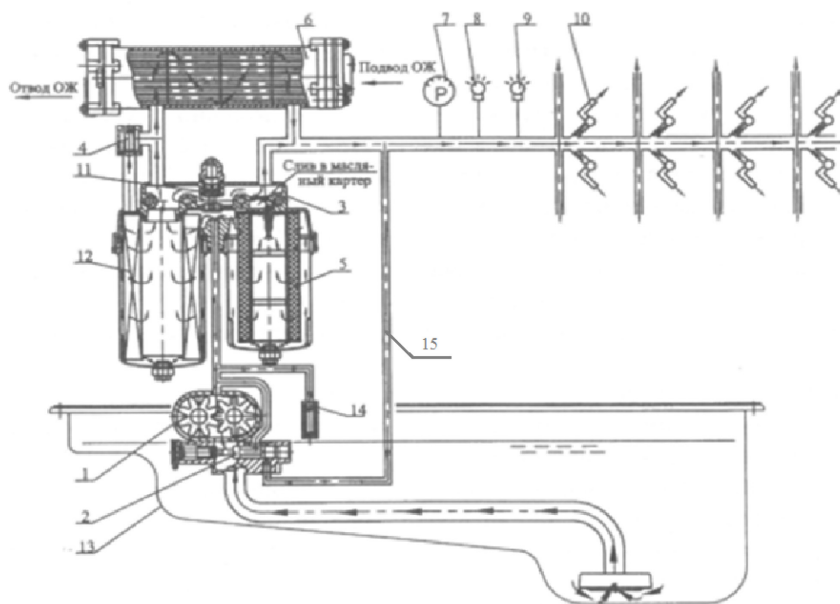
Схема смазочной системы двигателя КамАЗ-740.11 [6]:
